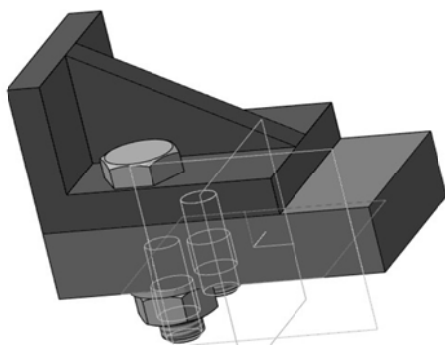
Готовая сборка, включая стандартные крепежные изделия
